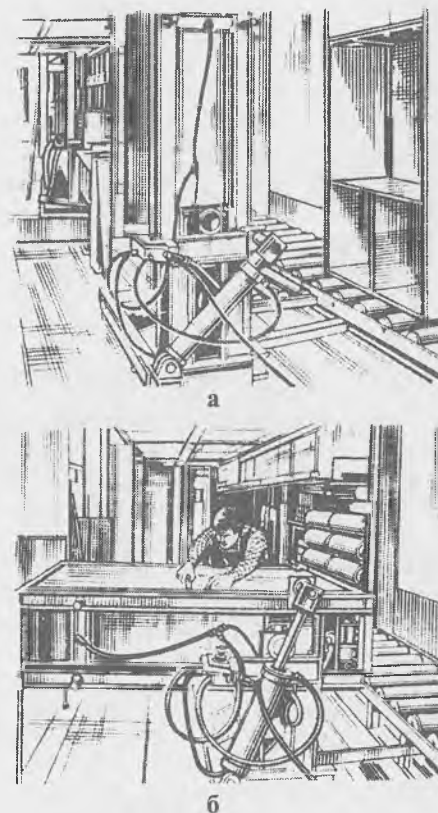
Стапельная сборка корпуса (а) и установка задней стенки (б)
